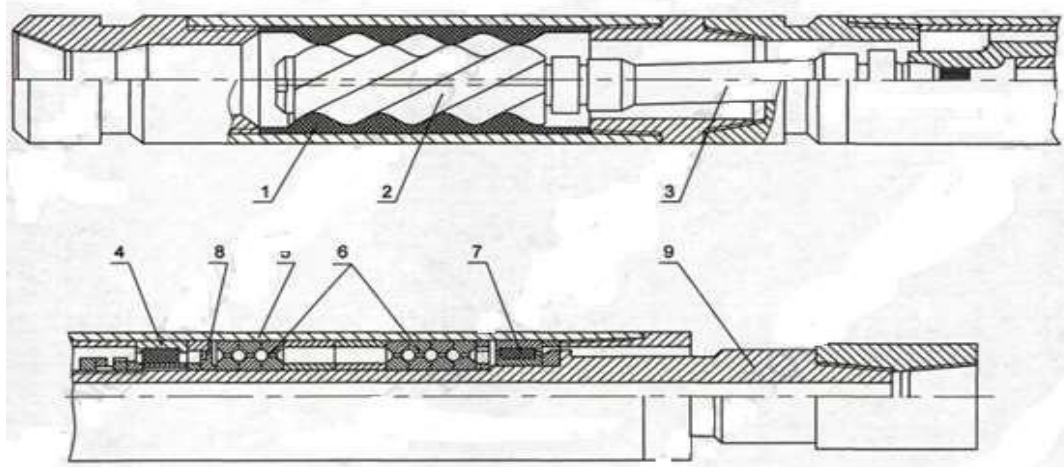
Типовая конструкция винтового забойного двигателя. 1 – статор; 2 – ротор; 3 – шарнирное соединение; 4,7- радиальные опоры; 5 – корпус шпинделя; 6 – осевая опора; 8 – торцевое уплотнение; 9 – вал шпинделя.
